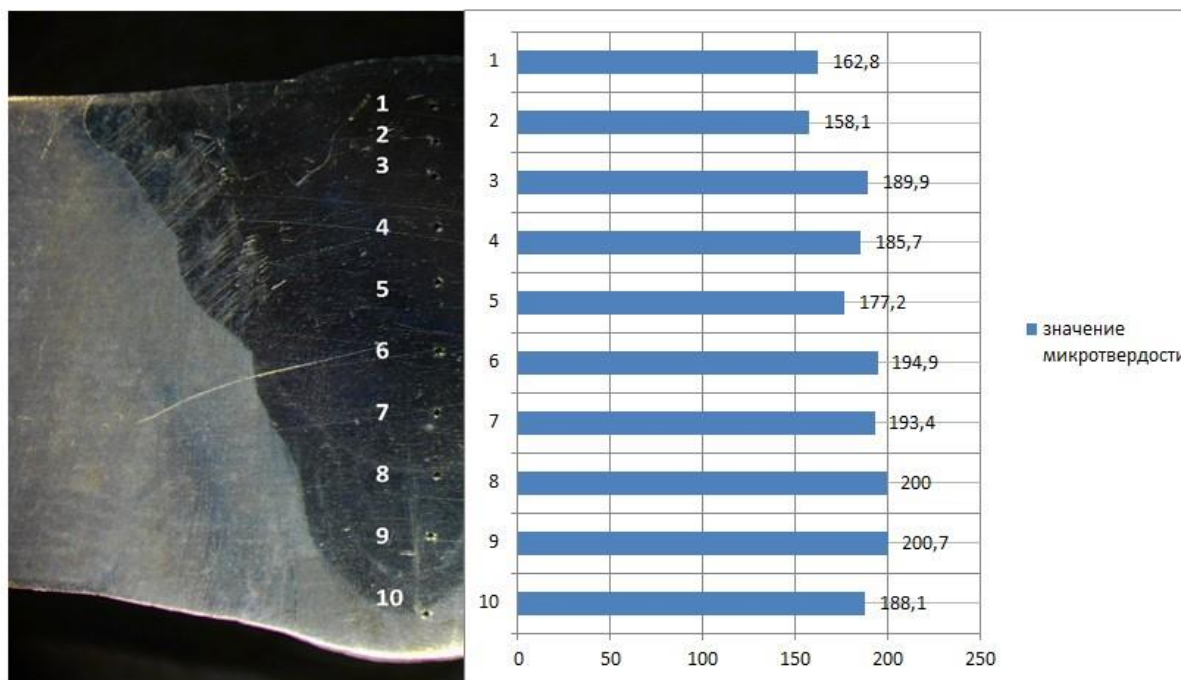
Микротвердость сварного шва образца варианта 2
